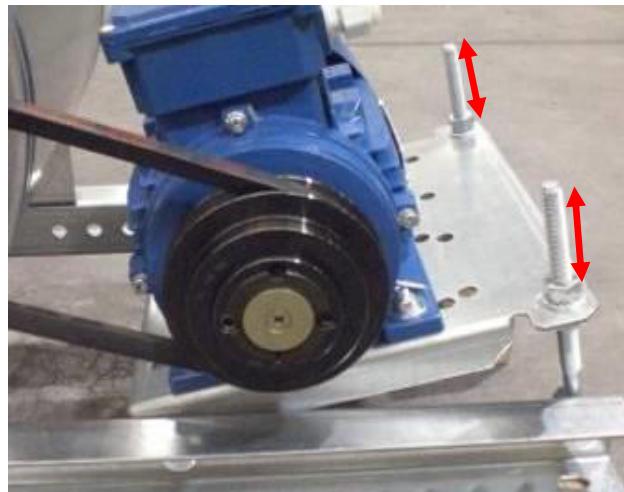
Регулировка шкивов с помощью резьбовых стержней
